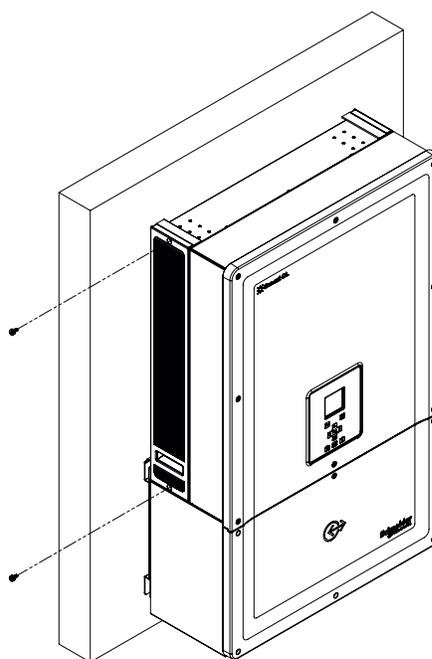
Desserrage des vis du couvercle de la grille d'aération – côté gauche
